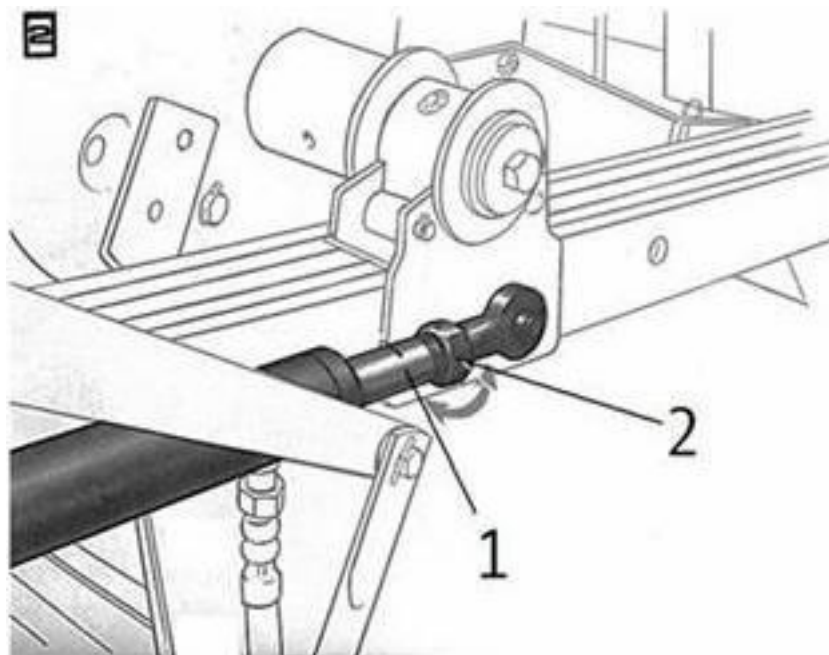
Схема регулировки положения мотовила по горизонтали:
